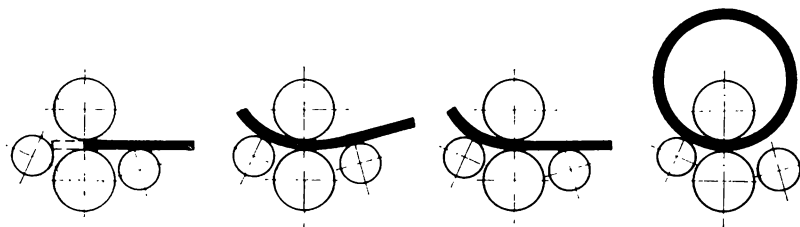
Гибка листовых деталей цилиндрической формы в листогибочных вальцах.
